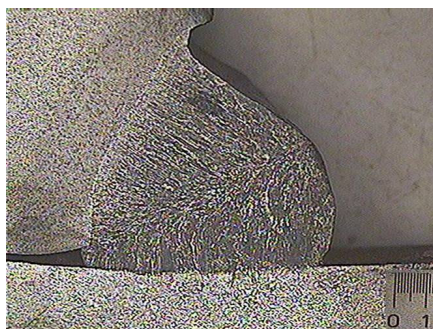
Falta de penetração na solda do gancho do quadro auxiliar
